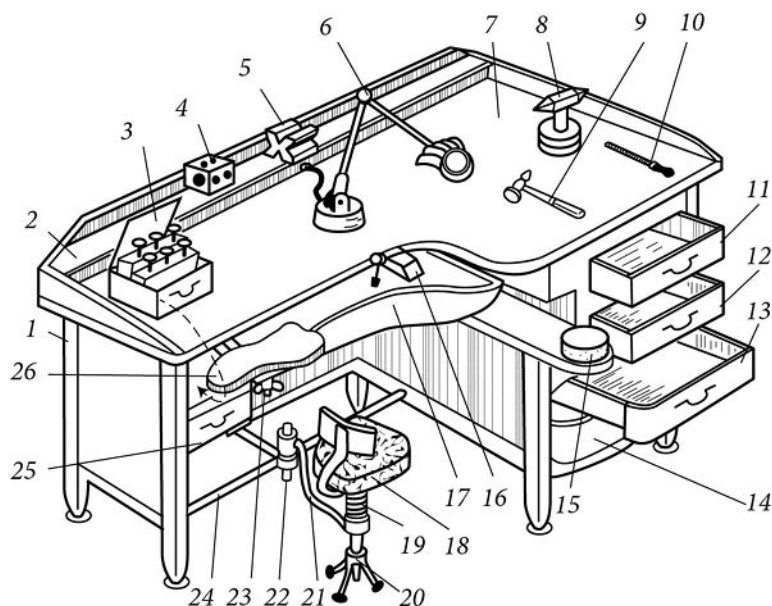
Универсальный ювелирно-граверный верстак: 1 – каркас; 2 – полочка; 3 – коробка с набором штихелей; 4, 5 – призмы; 6 – шарнирно-поворотная электролампа с линзой; 7 – столешница; 8 – настольная наковальня; 9 – место расположения молотков; 10 – место расположения напильников; 11–14 – выдвижные ящики; 15 – круглая наковальня; 16 – фенагель; 17 – выдвижной сборник; 18 – сиденье со спинкой; 19 – спиральная пружина стула; 20 – тренога стула; 21 – труба кронштейна; 22 – ось консоли; 23 – подъемно-регулируемый винт подлокотника; 24 – опора для ног (труба); 25 – коробка с инструментом; 26 – подлокотник.
